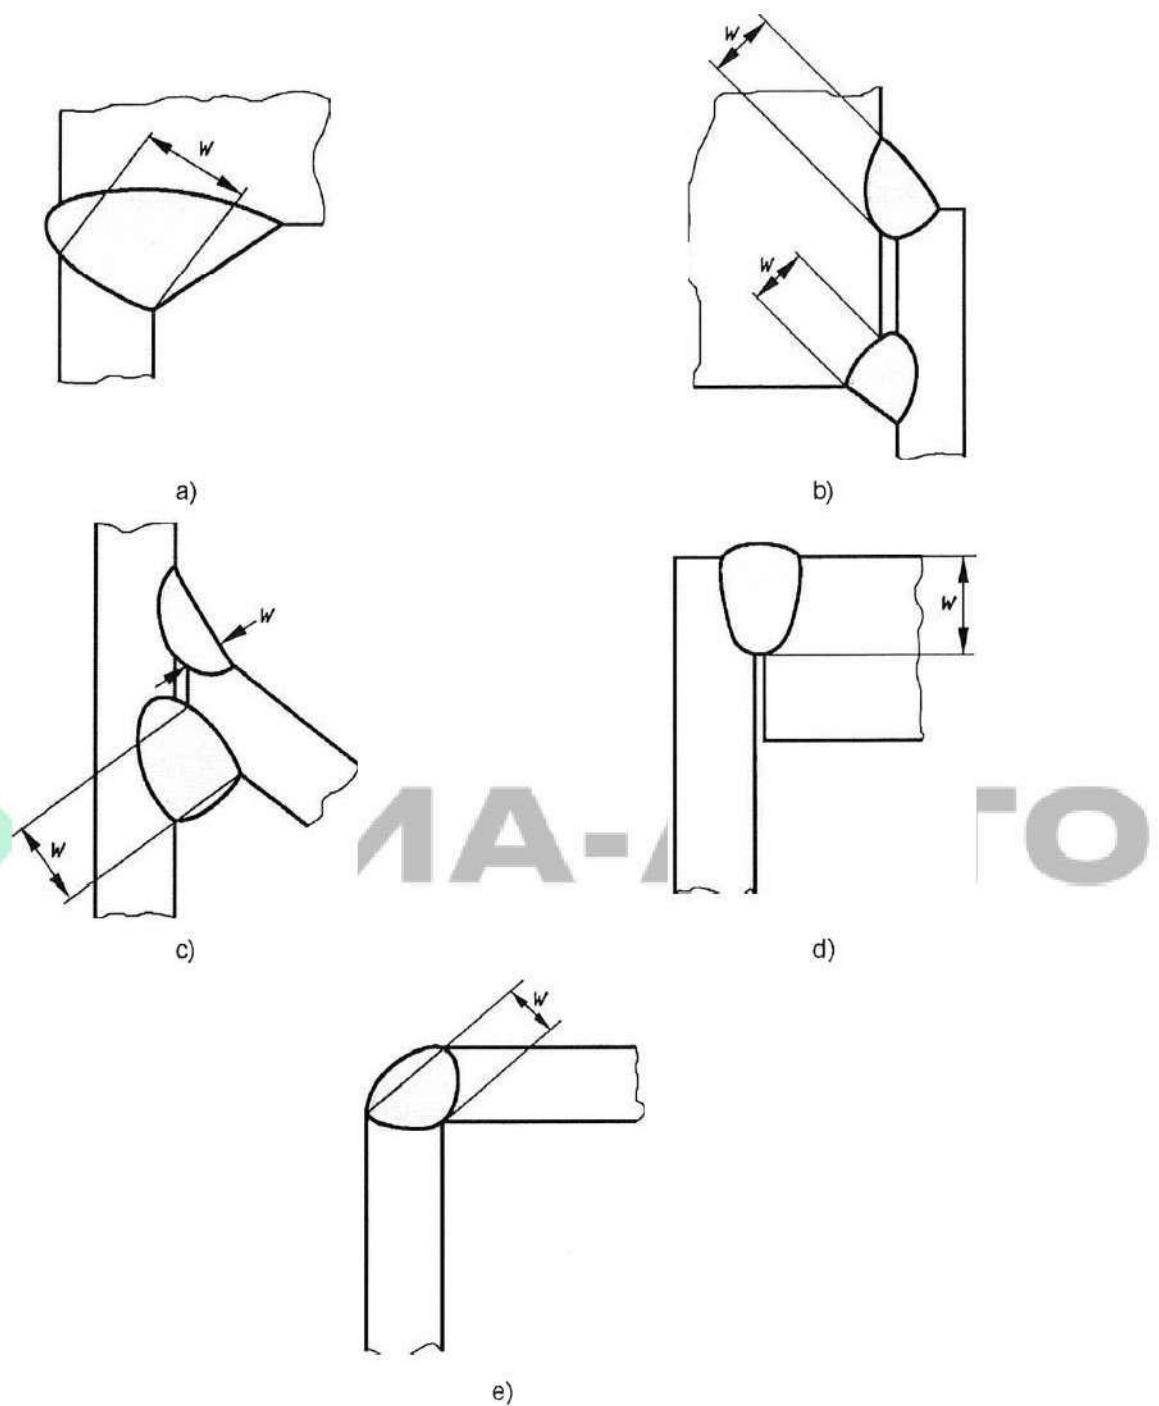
Типичные примеры эффективной глубины угловых сварных швов
